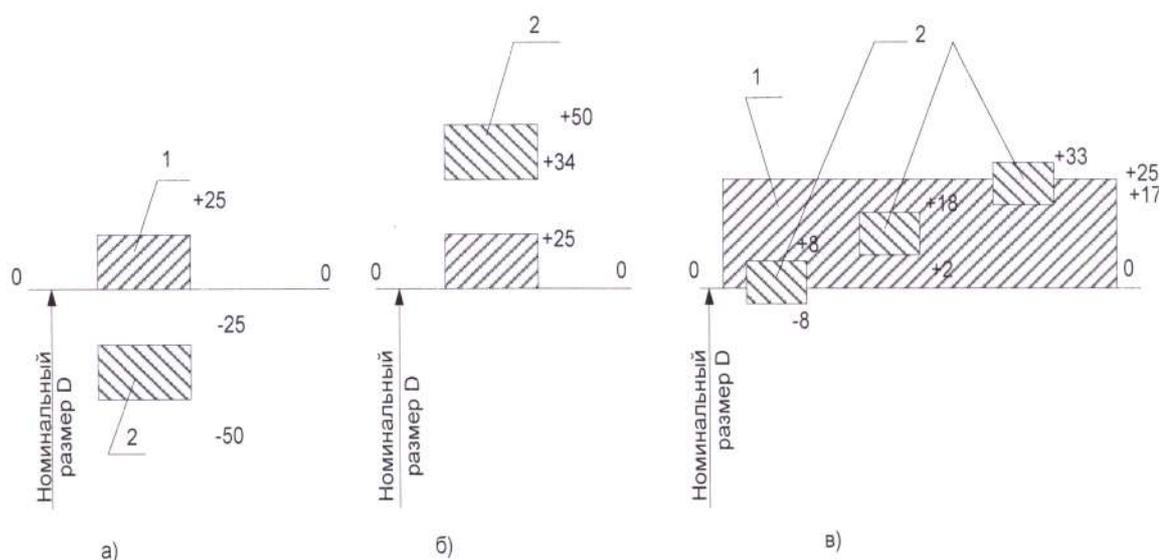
Поля допусков: отверстия-1 вала- 2.
